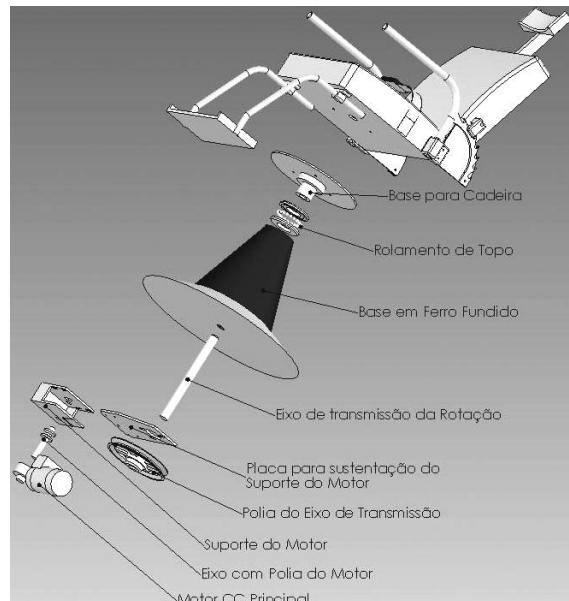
Vista explodida da CREC. Figure 2. Exploded view of the ECRC.
